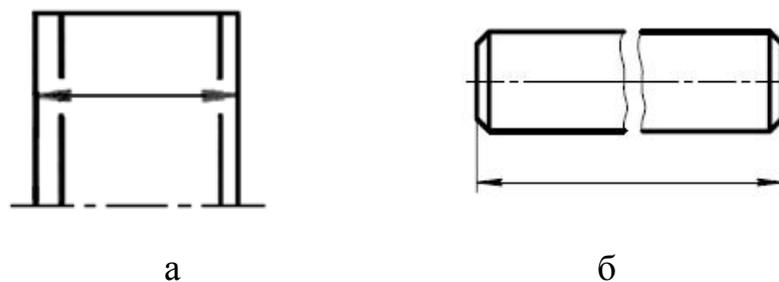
Нанесение размеров: а – при недостатке места для стрелки; б – при изображении изделий с разрывом
